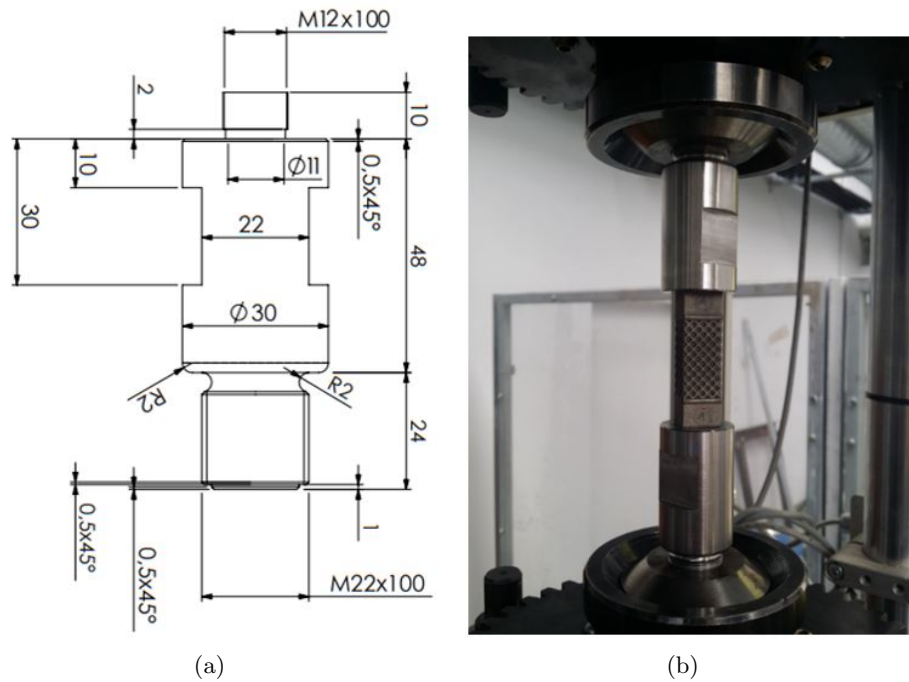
(a) Dimensions des pièces d'adaptation en mm et (b) montage des éprouvettes à la machine de fatigue.
